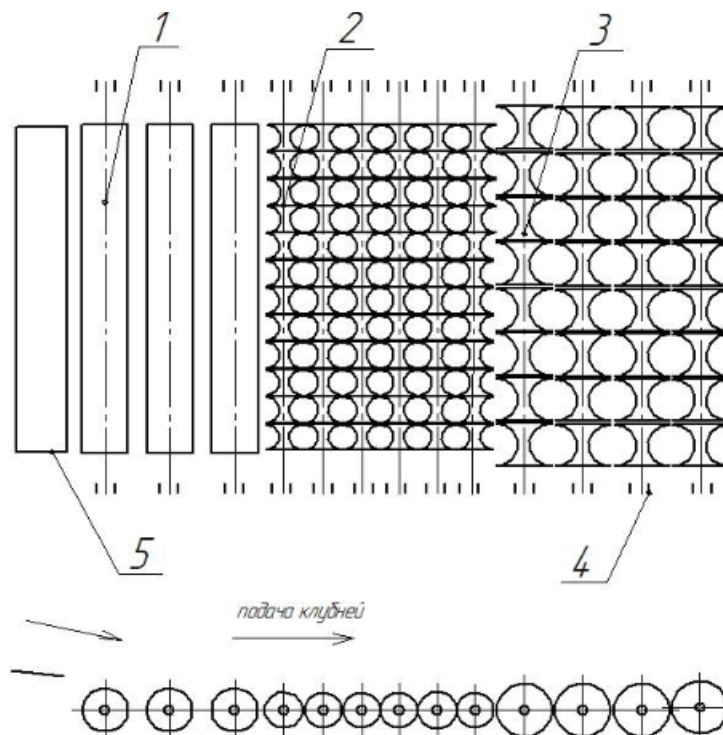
Схема работы сортировочной машины роликового типа:
